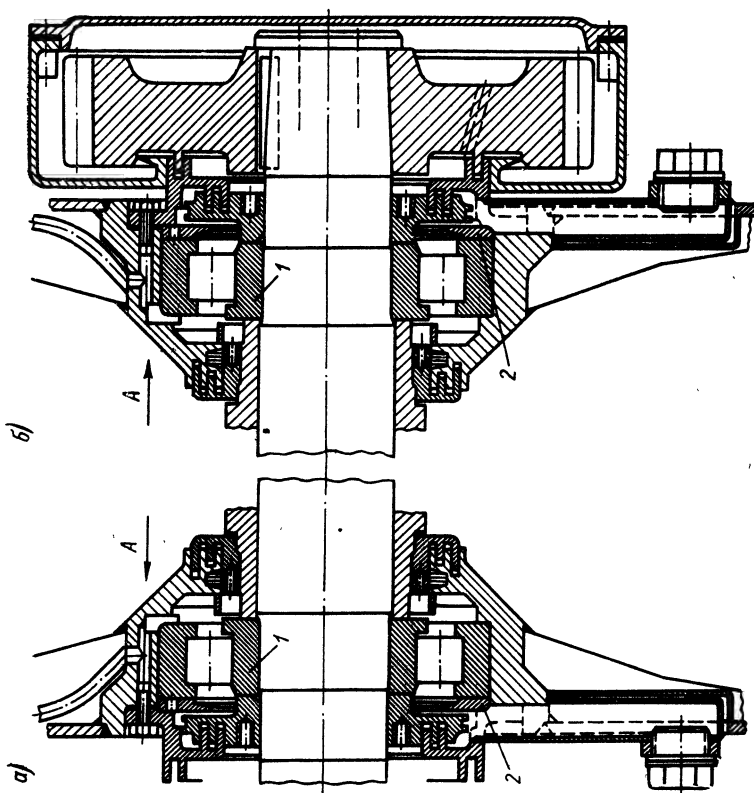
Узлы роликподшипников при двусторонней косозубой передаче: а — со стороны коллектора; б — со стороны, обратной коллектору
